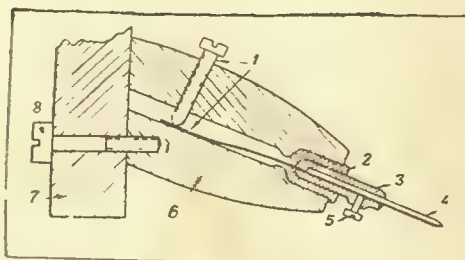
Способ крепления якоря в адаптере т. Федорова: 1—струна, держащая якорь, и винт крепления струны; 2—резина; 3—якорь; 4—игла; 5—винт крепления иглы; 6—тело магнитопровода; 7—полюс магнита; 8—винт крепления детали 6
